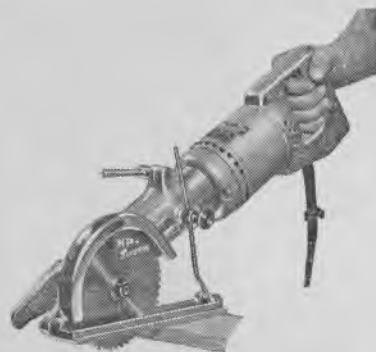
Rundsav, med en boremaskine som drivkraft. (Jordrup Maskinsnedkeri).
